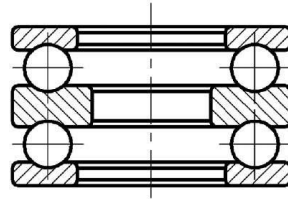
Дворядний упорний кульковий підшипник
